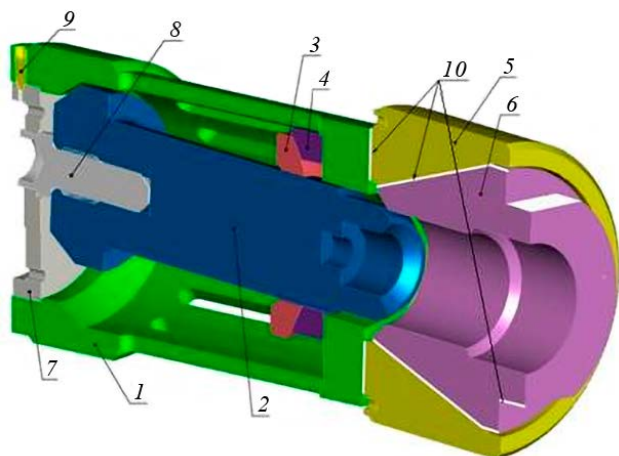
Общий вид ГО в сборе: 1 — картридж; 2 — болт центральный; 3 — шайба сферическая; 4 — шайба коническая; 5 — втулка конусная; 6 — гайка конусная; 7 — крышка; 8 — палец; 9 — винт крепления; 10 — ЭИП
